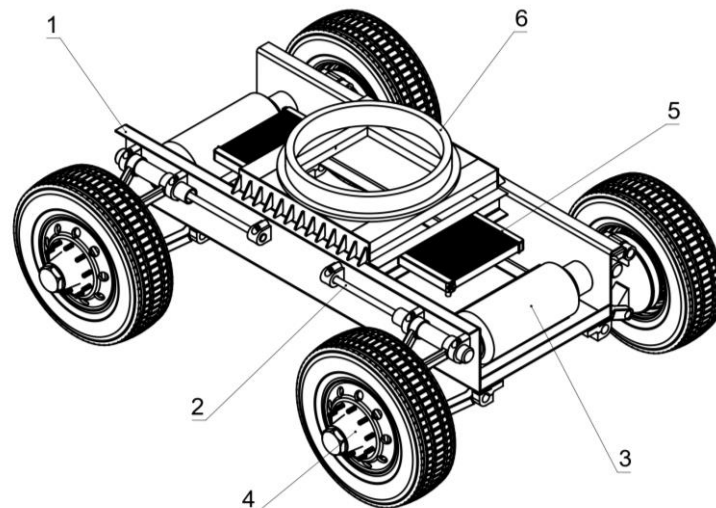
Зовнішній 3D вигляд поворотної платформи: 1 – рама; 2 – торсіонна підвіска; 3 – модуль ступеневої електромеханічної трансмісії; 4 – колесо з колісним редуктором; 5 – радіатор; 6 – погон поворотної платформи
